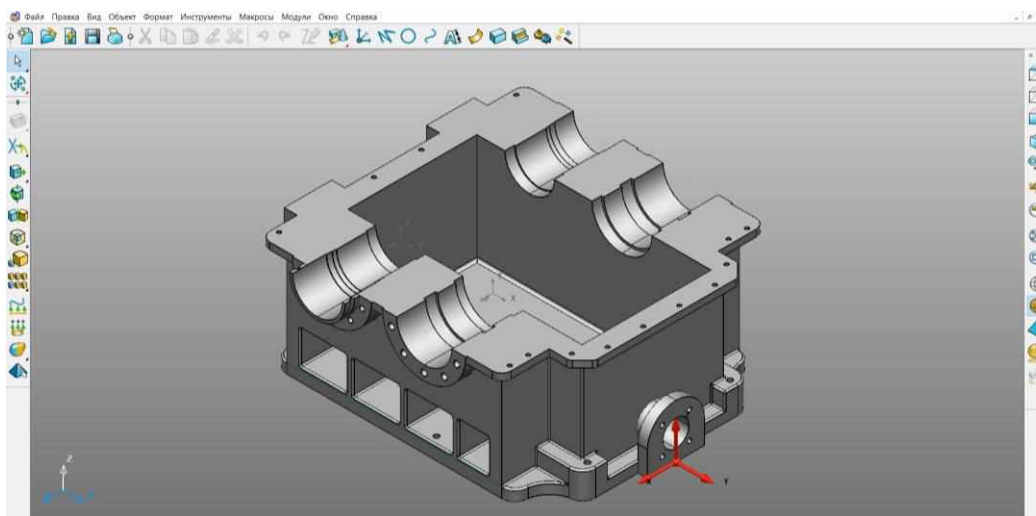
3D-модель корпусу редуктора побудована у середовищі САПР PowerSHAPE
